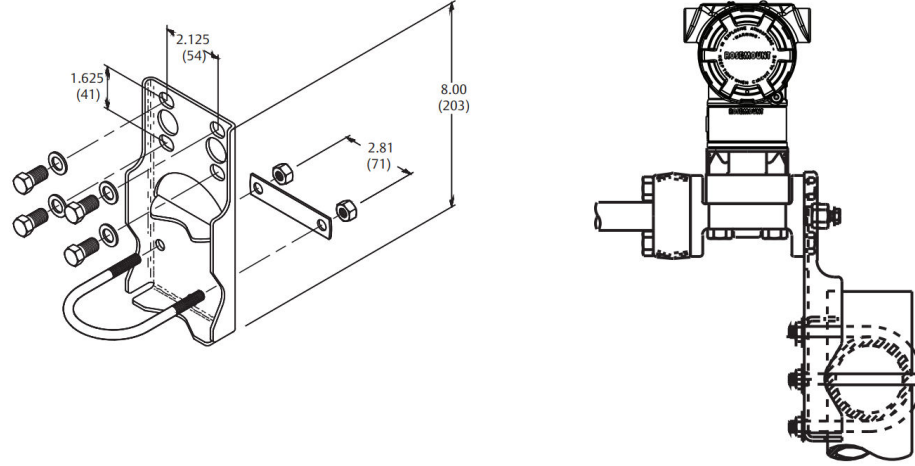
Panel montaj braketi opsiyon kodları B2 ve B8
